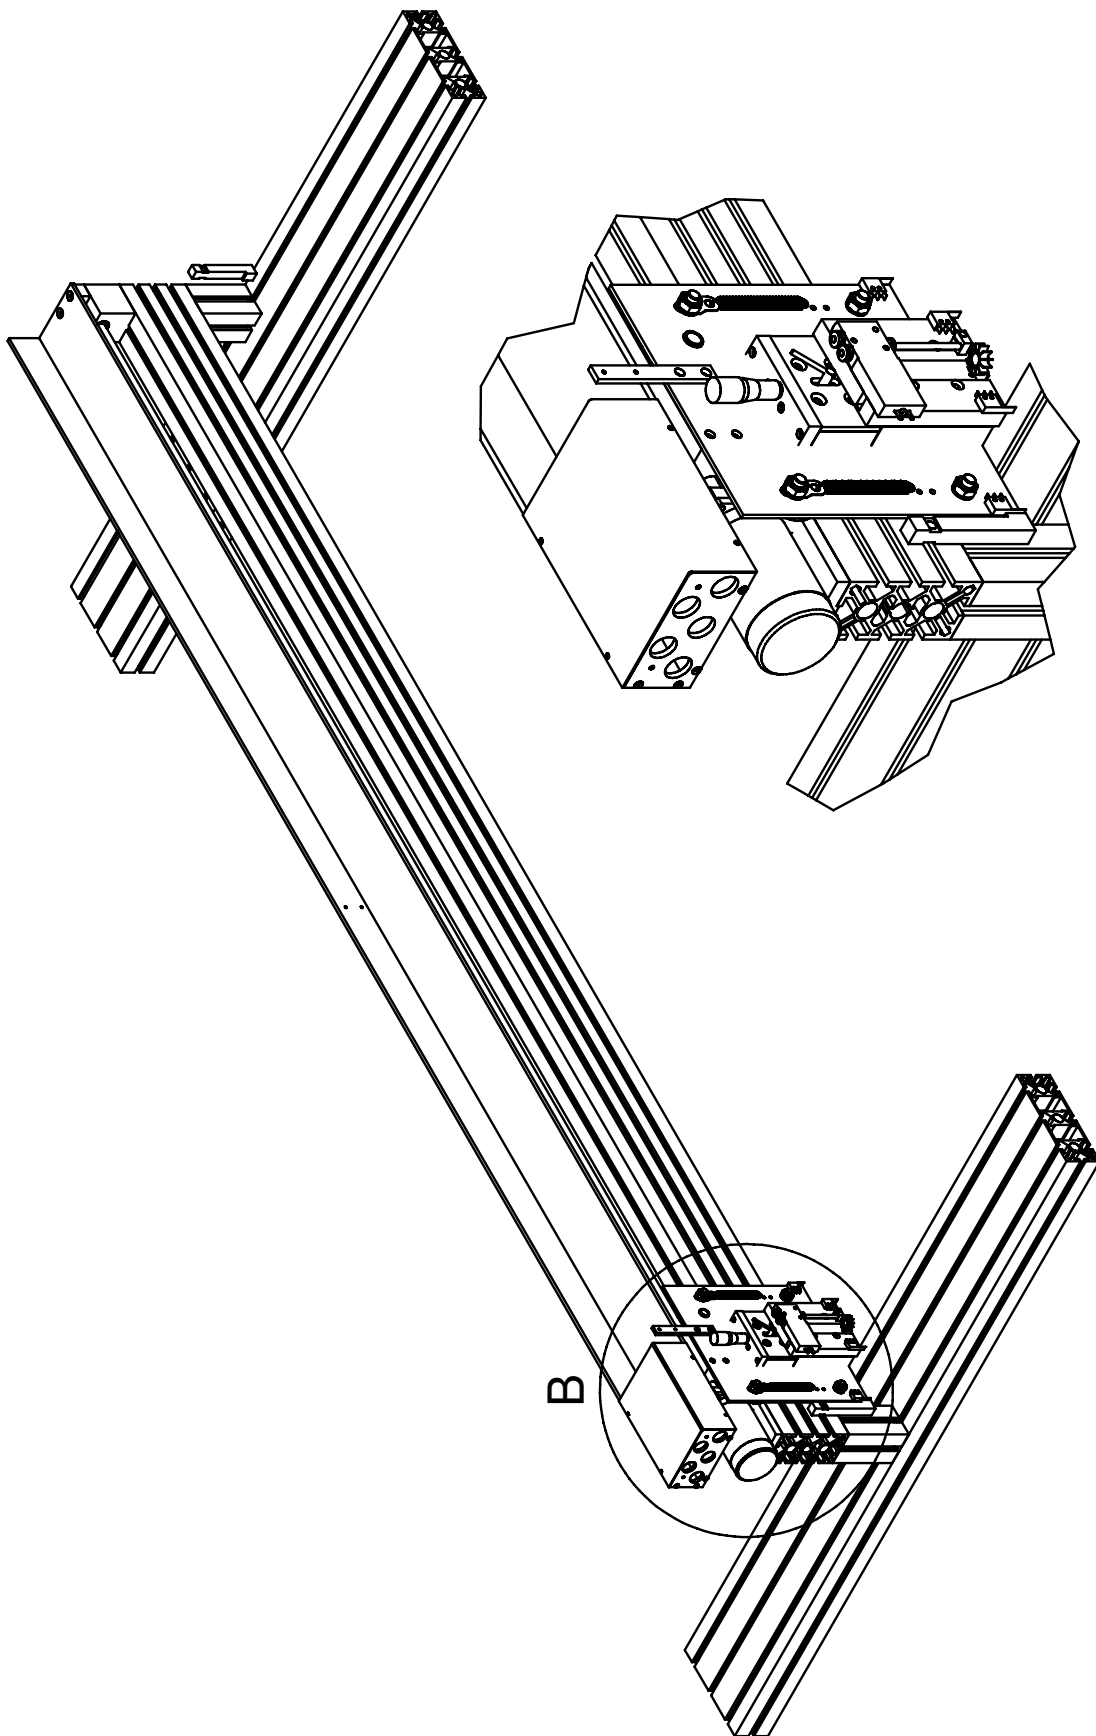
Stückplan und Zeichnung der Testmaschine. Im Ausschnitt sind zwei Muttern gezeigt, welche das Laufspiel des Laufwagens vermeiden sollen.
